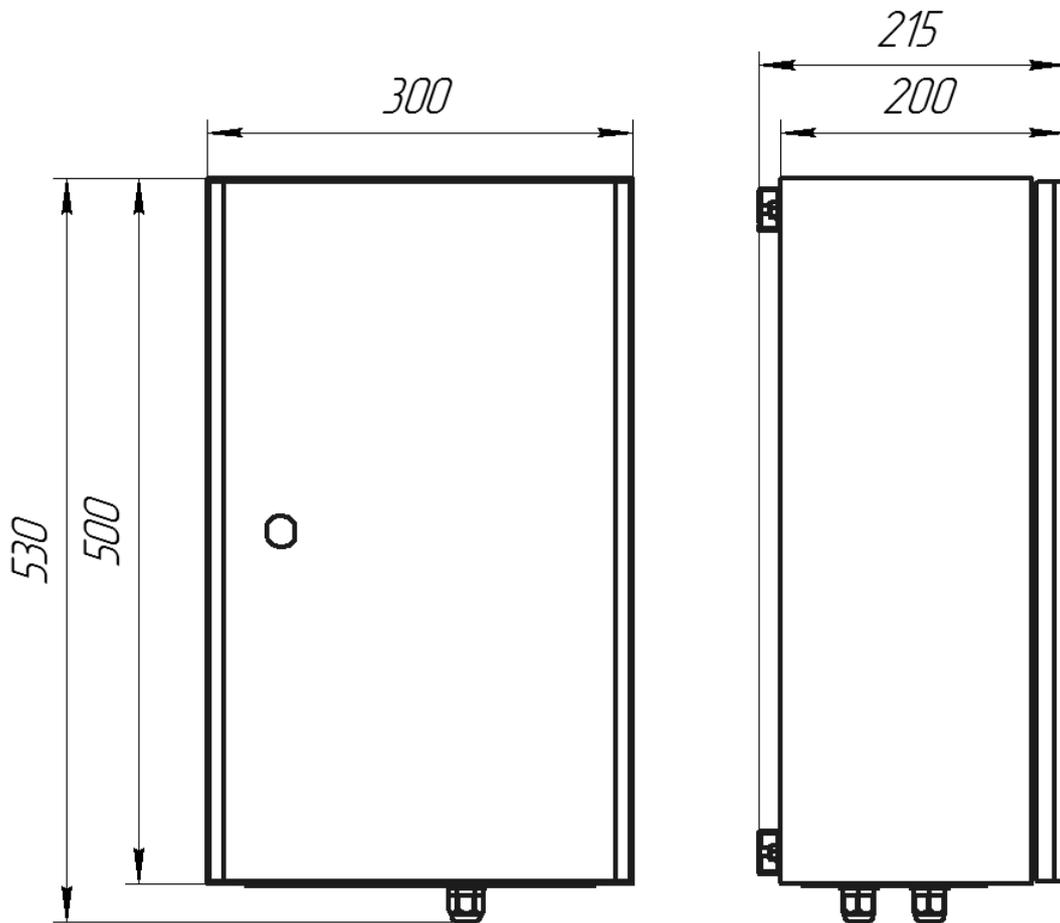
Габаритные размеры блока БСПИ-3ТН
